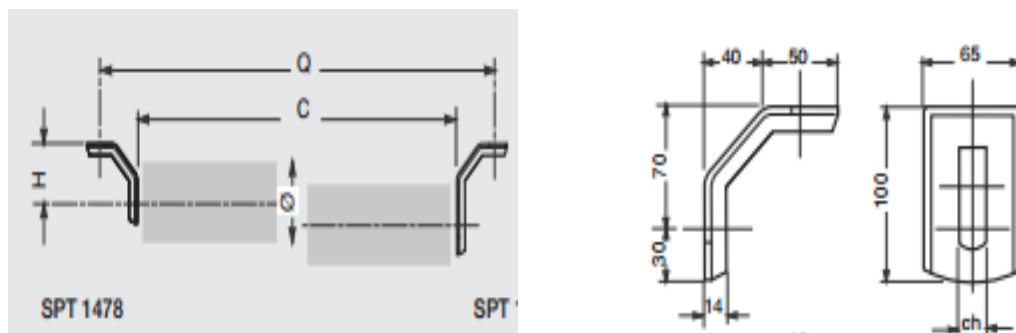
Dimensions des pattes de fixation " SPT1478"
